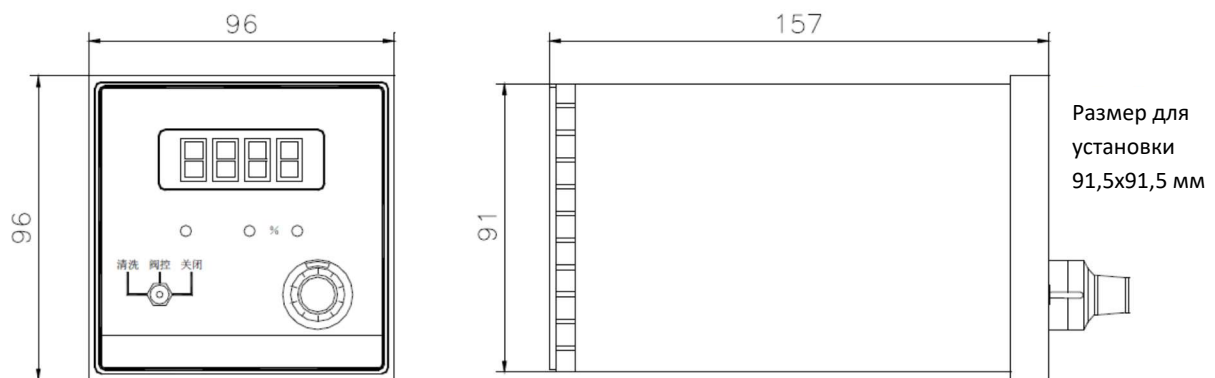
Габаритные размеры корпуса контроллеров D08-1F, 1FP, 1FM
